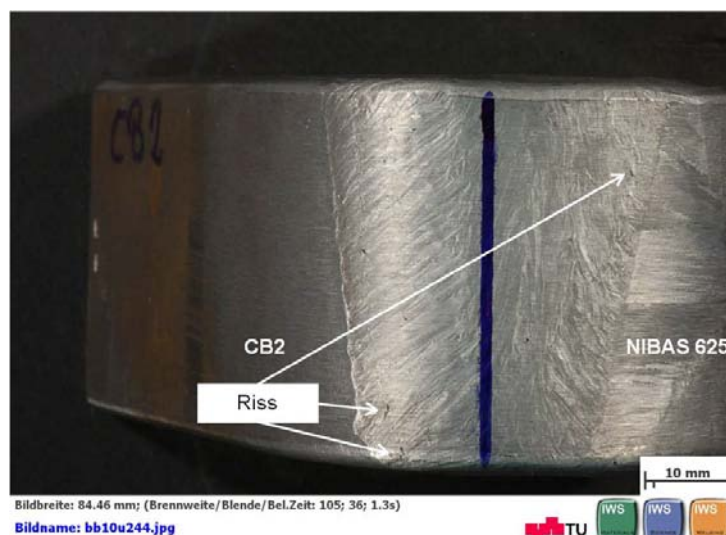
Gebogene Seitenbiegeprobe (4. Probeschweißung - Fülldrahtelektrode); geführter Seitenbiegeversuch.
